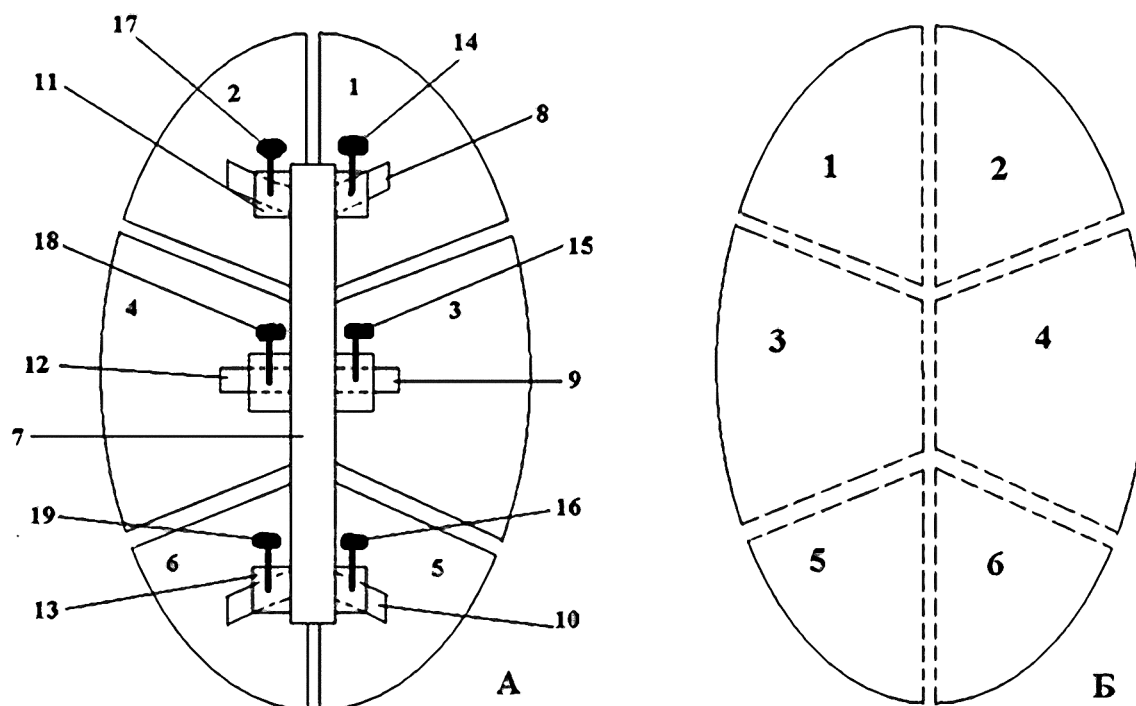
Устройство для изготовления акриловых препаратов рельефа черепа (А – вид устройства снизу; Б – вид устройства сверху): 1,2 – передние части корпуса; 3,4 – средние части корпуса; 5,6 – задние части корпуса; 7 – ручка; 8,9,10 – поперечные балки (коромысла); 11,12,13 – поперечные пластинки; 14,15,16,17,18,19 – поперечные стержни-рычаги
